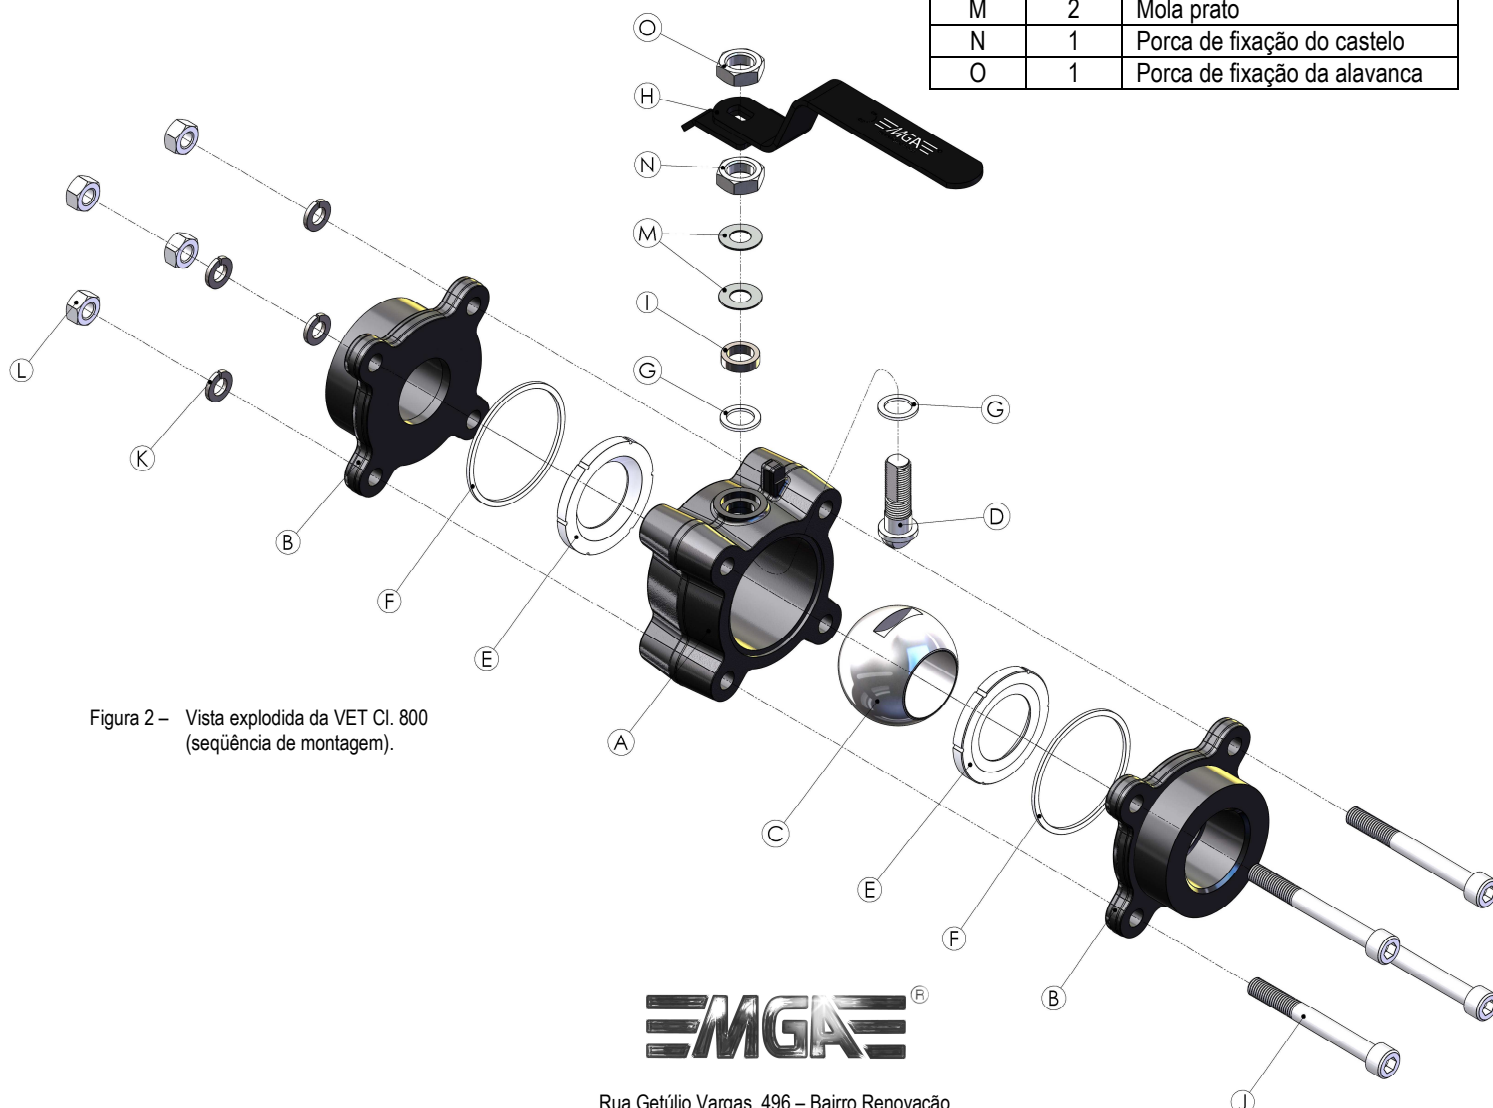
Vista explodida da VET CI. 800 (seqüência de montagem).
